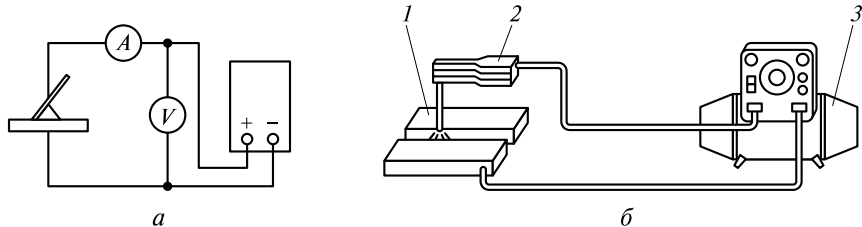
Схема питания дуги при ручной дуговой сварке покрытым электродом:
